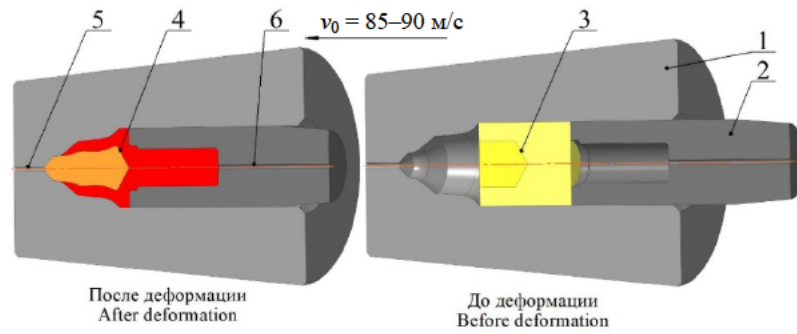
Схема деформирования для скоростного горячего выдавливания биметаллических полуфабрикатов детали «тангенциальный резец»: 1 – полуматрица; 2 – формообразующий пуансон; 3 – составная заготовка; 4 – биметаллический полуфабрикат; 5, 6 – газоотводящие каналы
